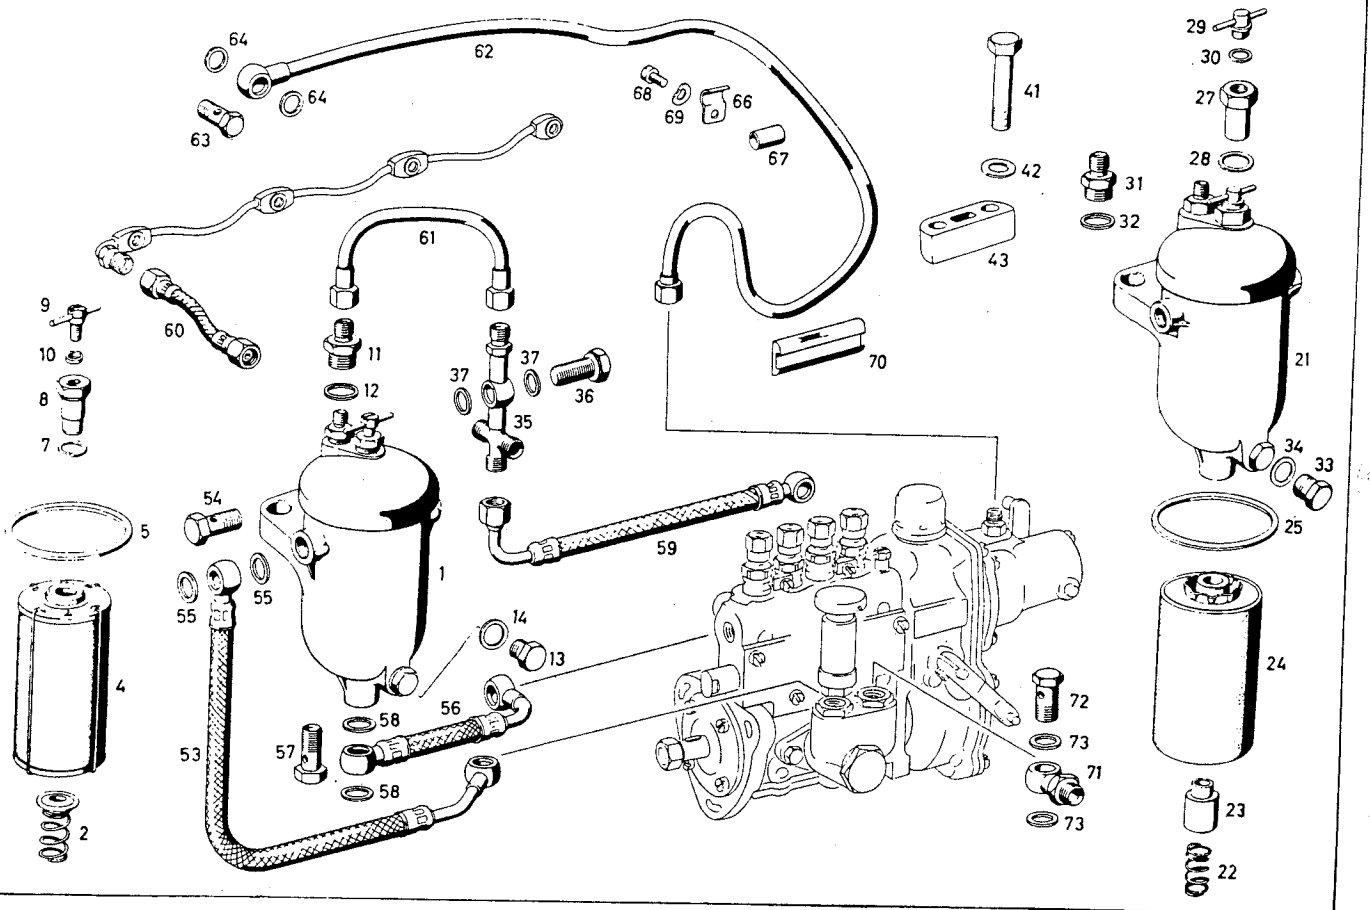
Kraftstoff-Filter mit Zu- und Ableitungen, zerlegt (OM 621)
